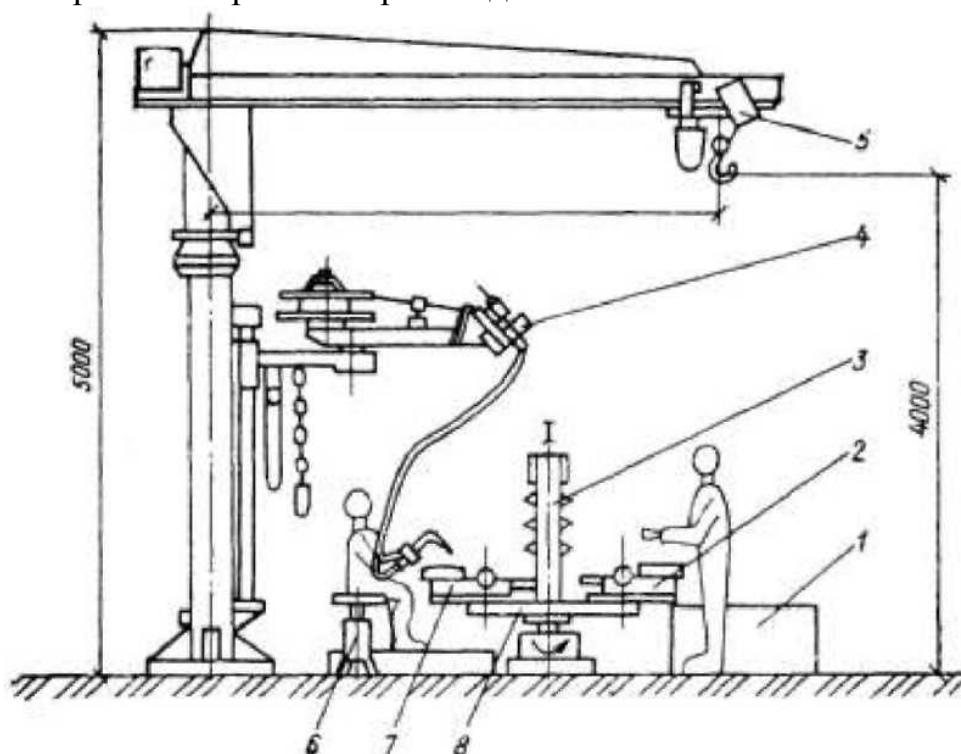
Схема расположения оборудования на рабочем месте слесаря-сборщика и электросварщика: 1 – ящик с заготовками; 2, 7 – приспособления сборочно-сварочные; 3 – ширма со встроенной вентиляцией; 4 – полуавтомат с консолью; 5 – кран консольно-поворотный; 6 – стул поворотный; 8 – стол двухпозиционный поворотный
